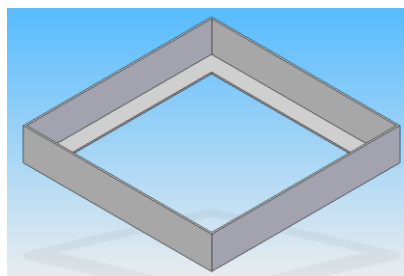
Plano y pieza sólida de la baldosa de concreto elegida.
